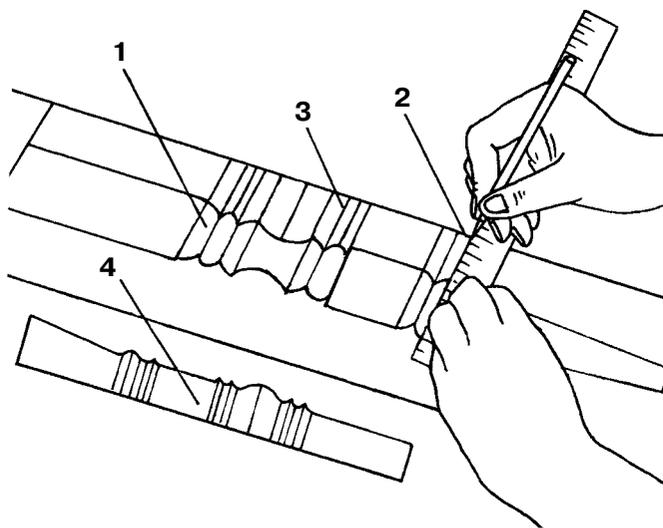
Подготовка разметки и изготовление шаблона с чертежа:
